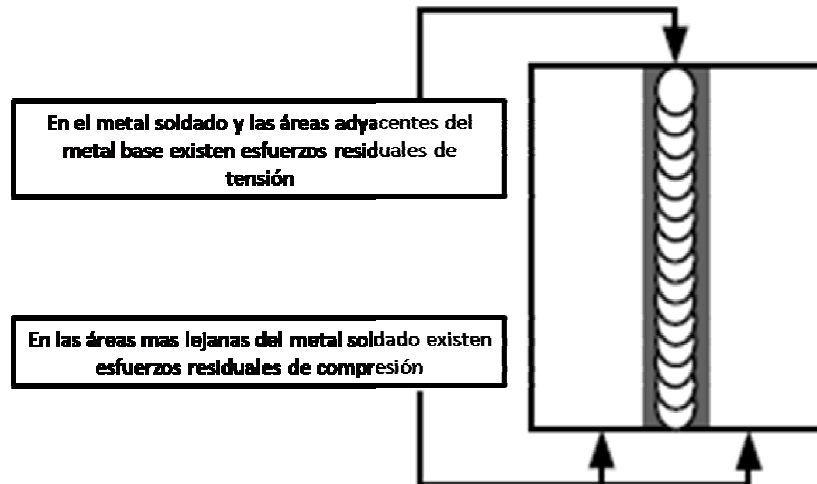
Placas de acero unidas por un cordón de soldadura [7]
